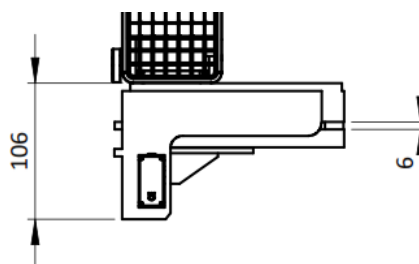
Esquema lateral izquierdo dimensional del sistema óptico de la impresora.
